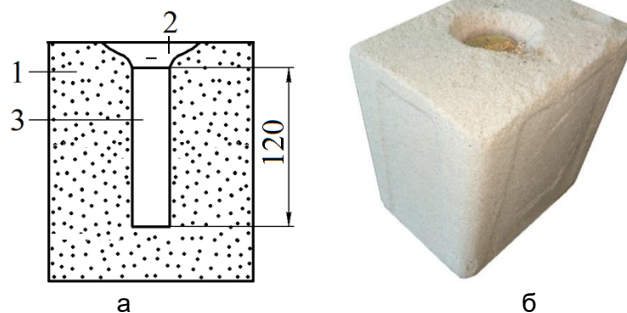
Схема ПРФ для виготовлення зразків циліндричної форми $\varnothing 30 \times 120$ мм (а) та загальний вигляд залитої ПРФ (б): 1 – ливарна форма; 2 – ливникова воронка; 3 – робоча порожнина ПРФ
